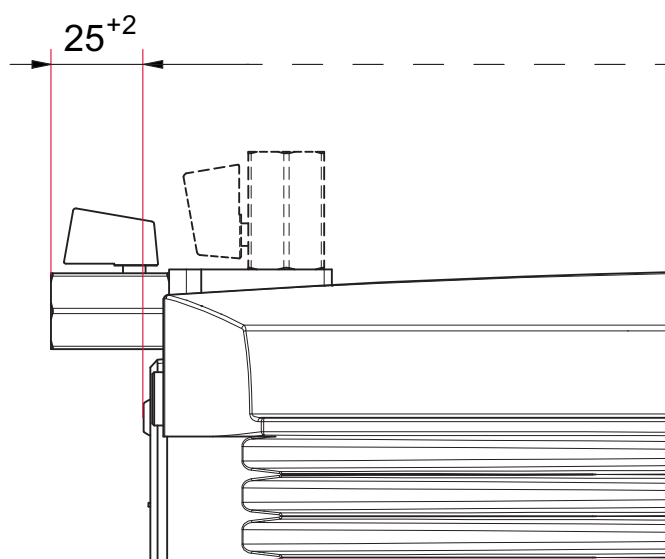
Dimensions de la vanne à boisseau sphérique pour la version de gaz corrosif
